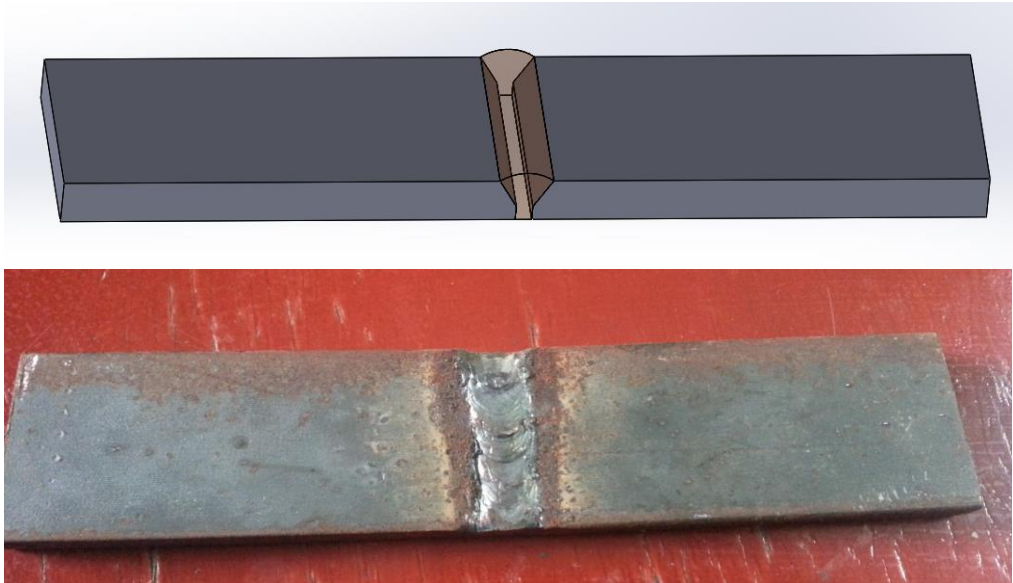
Probeta luego de retirar las secciones de inicio y fin del cordón de soldadura.
